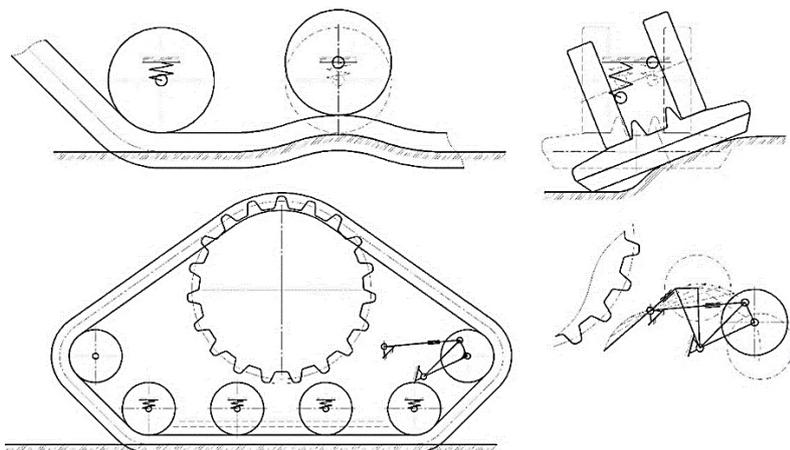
Кинематическая схема СГХС с системой подрессоривания катков / Fig. 3. Kinematic diagram with variable bearing surface area and roller suspension system
